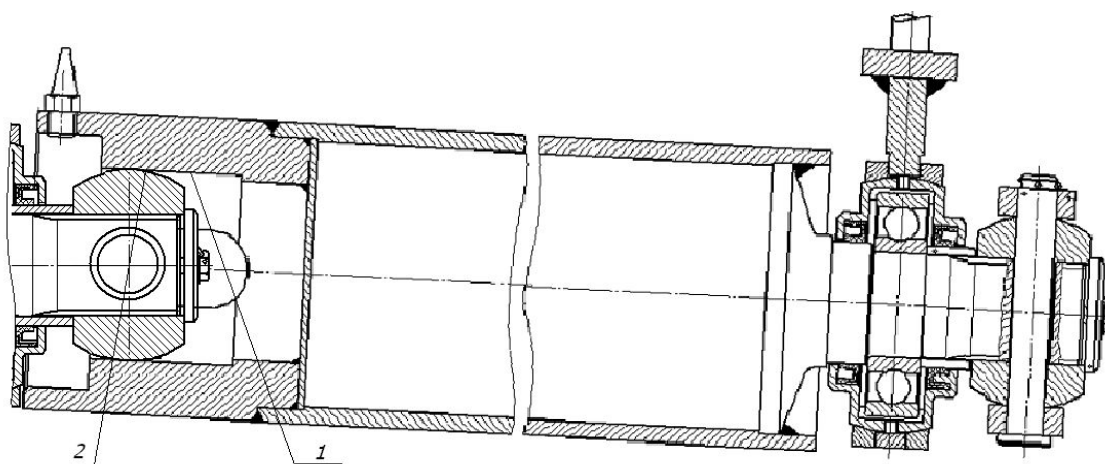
Схема разворота фрезы из-за неровностей на поверхности торфяной залежи
